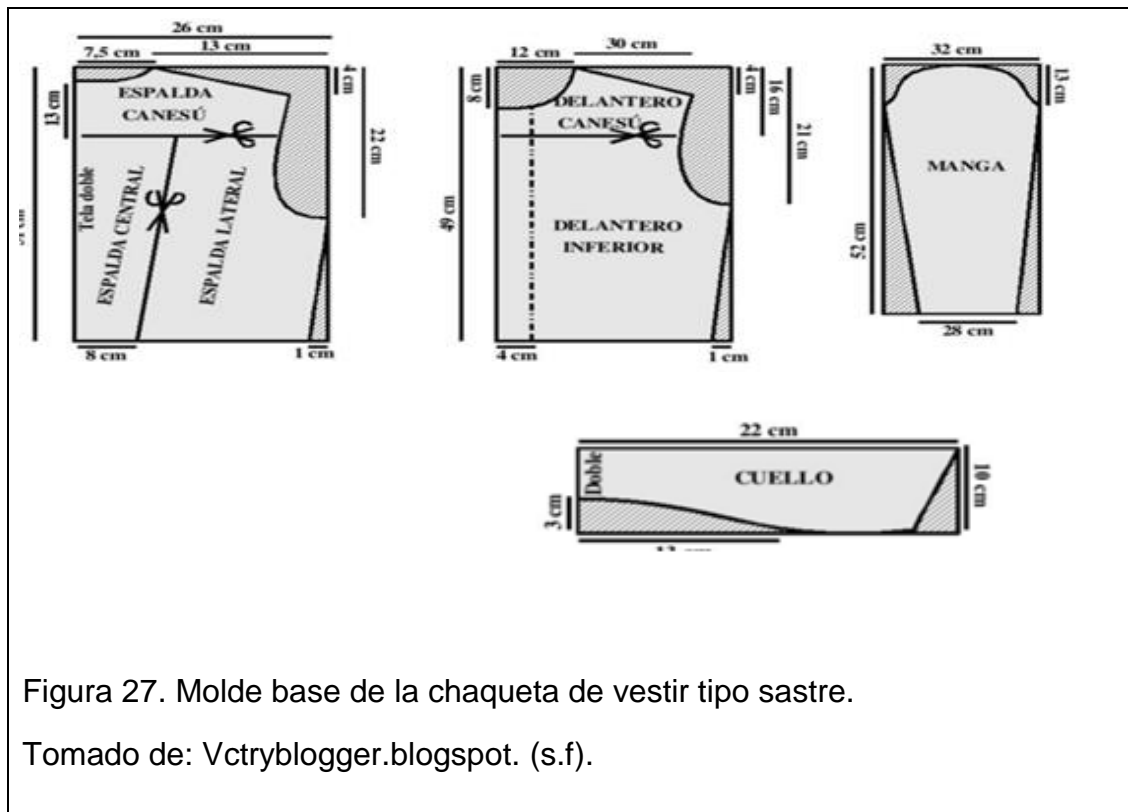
Molde base de la chaqueta de vestir tipo sastre.
